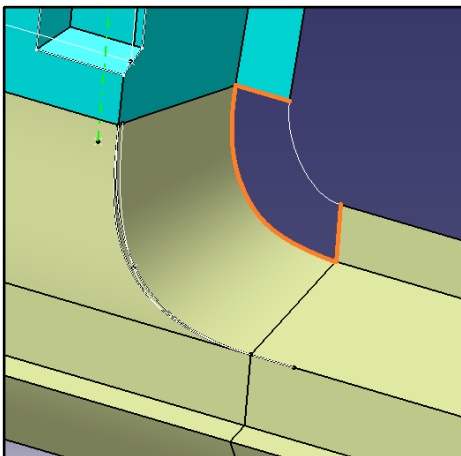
Spline-Definition für Schweißflanschübergang
